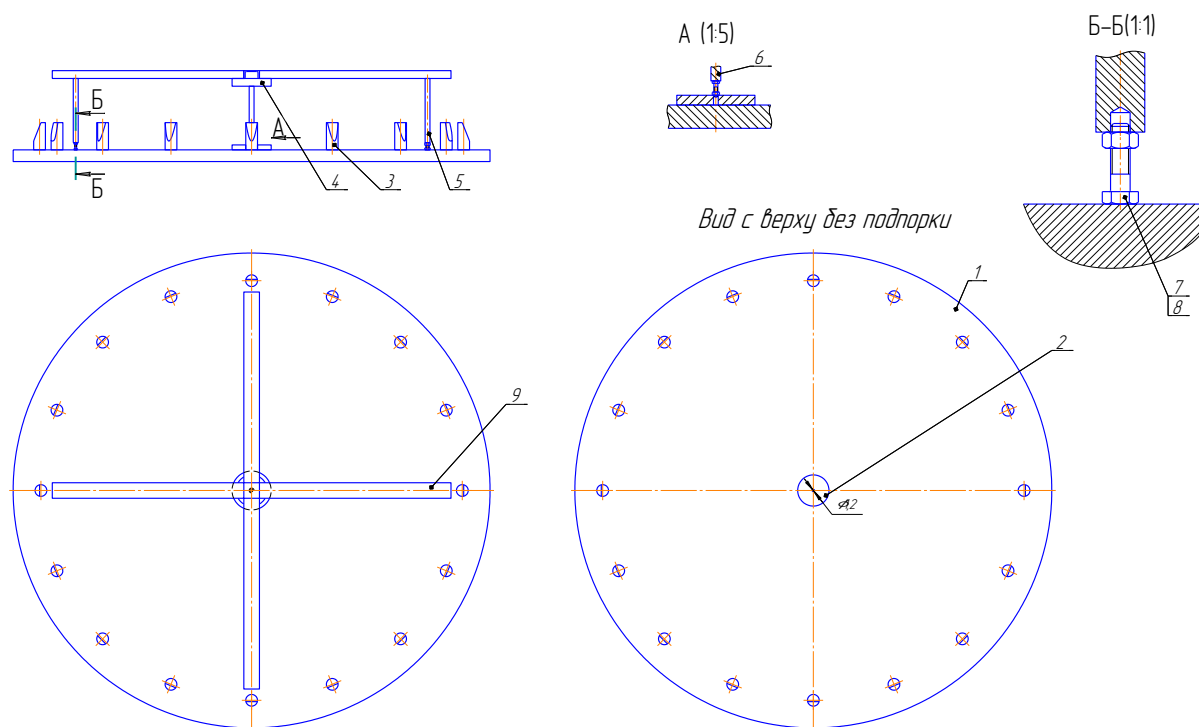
Устройство приспособления сборочно-сварочного
